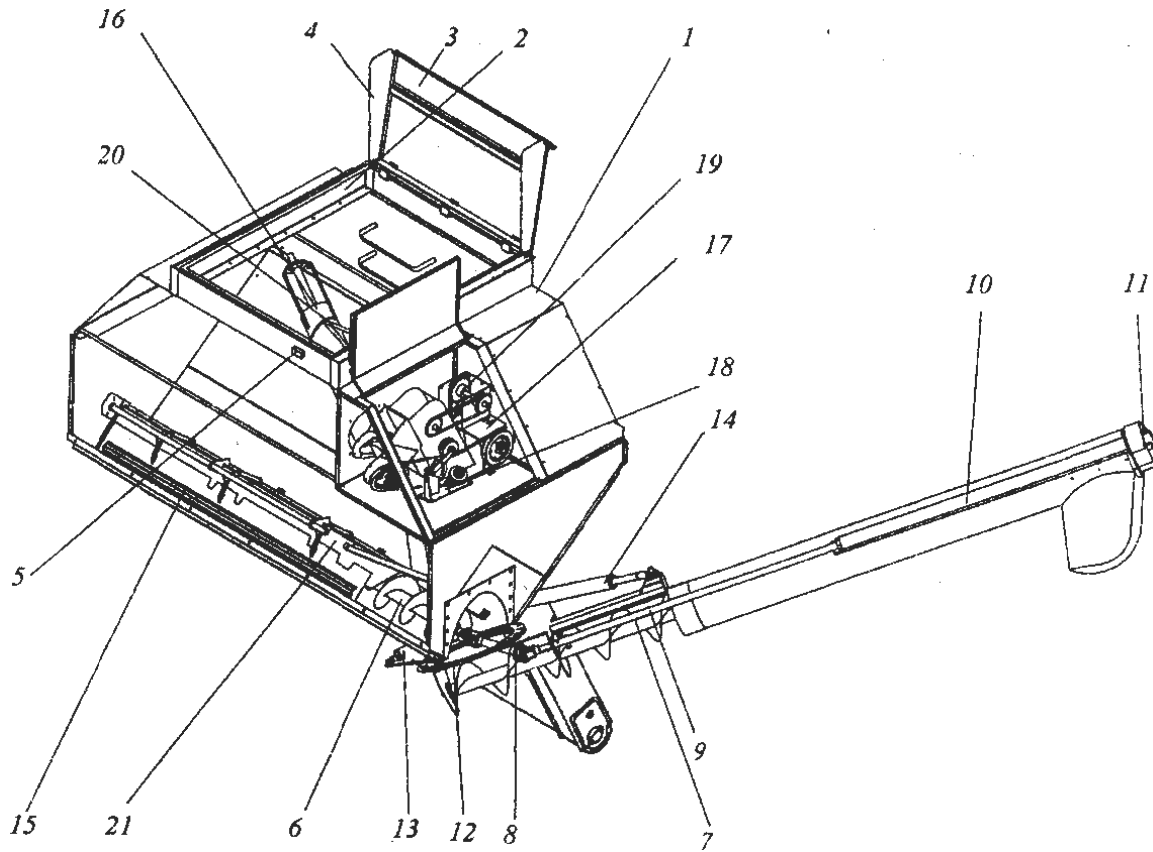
Бункер, загрузочный тракт и выгрузное устройство: 1 – бункер; 2 – надставка бункера; 3 – створка крыши; 4 – бортик; 5 – выключатель концевой; 6 – шнек горизонтальный; 7 – шнек наклонный; 8 – шарнир; 9 – вал приводной; 10 – кожух; 11 – передача цепная; 12 – фланец; 13, 14 – гидроцилиндры; 15 – заслонка; 16 – загрузочный шнек; 17 – привод загрузочного тракта; 18 – механизм привода; 19 – муфта зубчатая; 20 – растяжки; 21 – кожух
